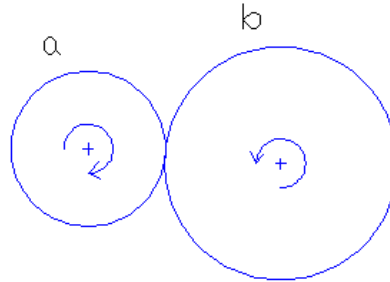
Sentido de giro del par de engranes (Piñón a - Engrane b)
